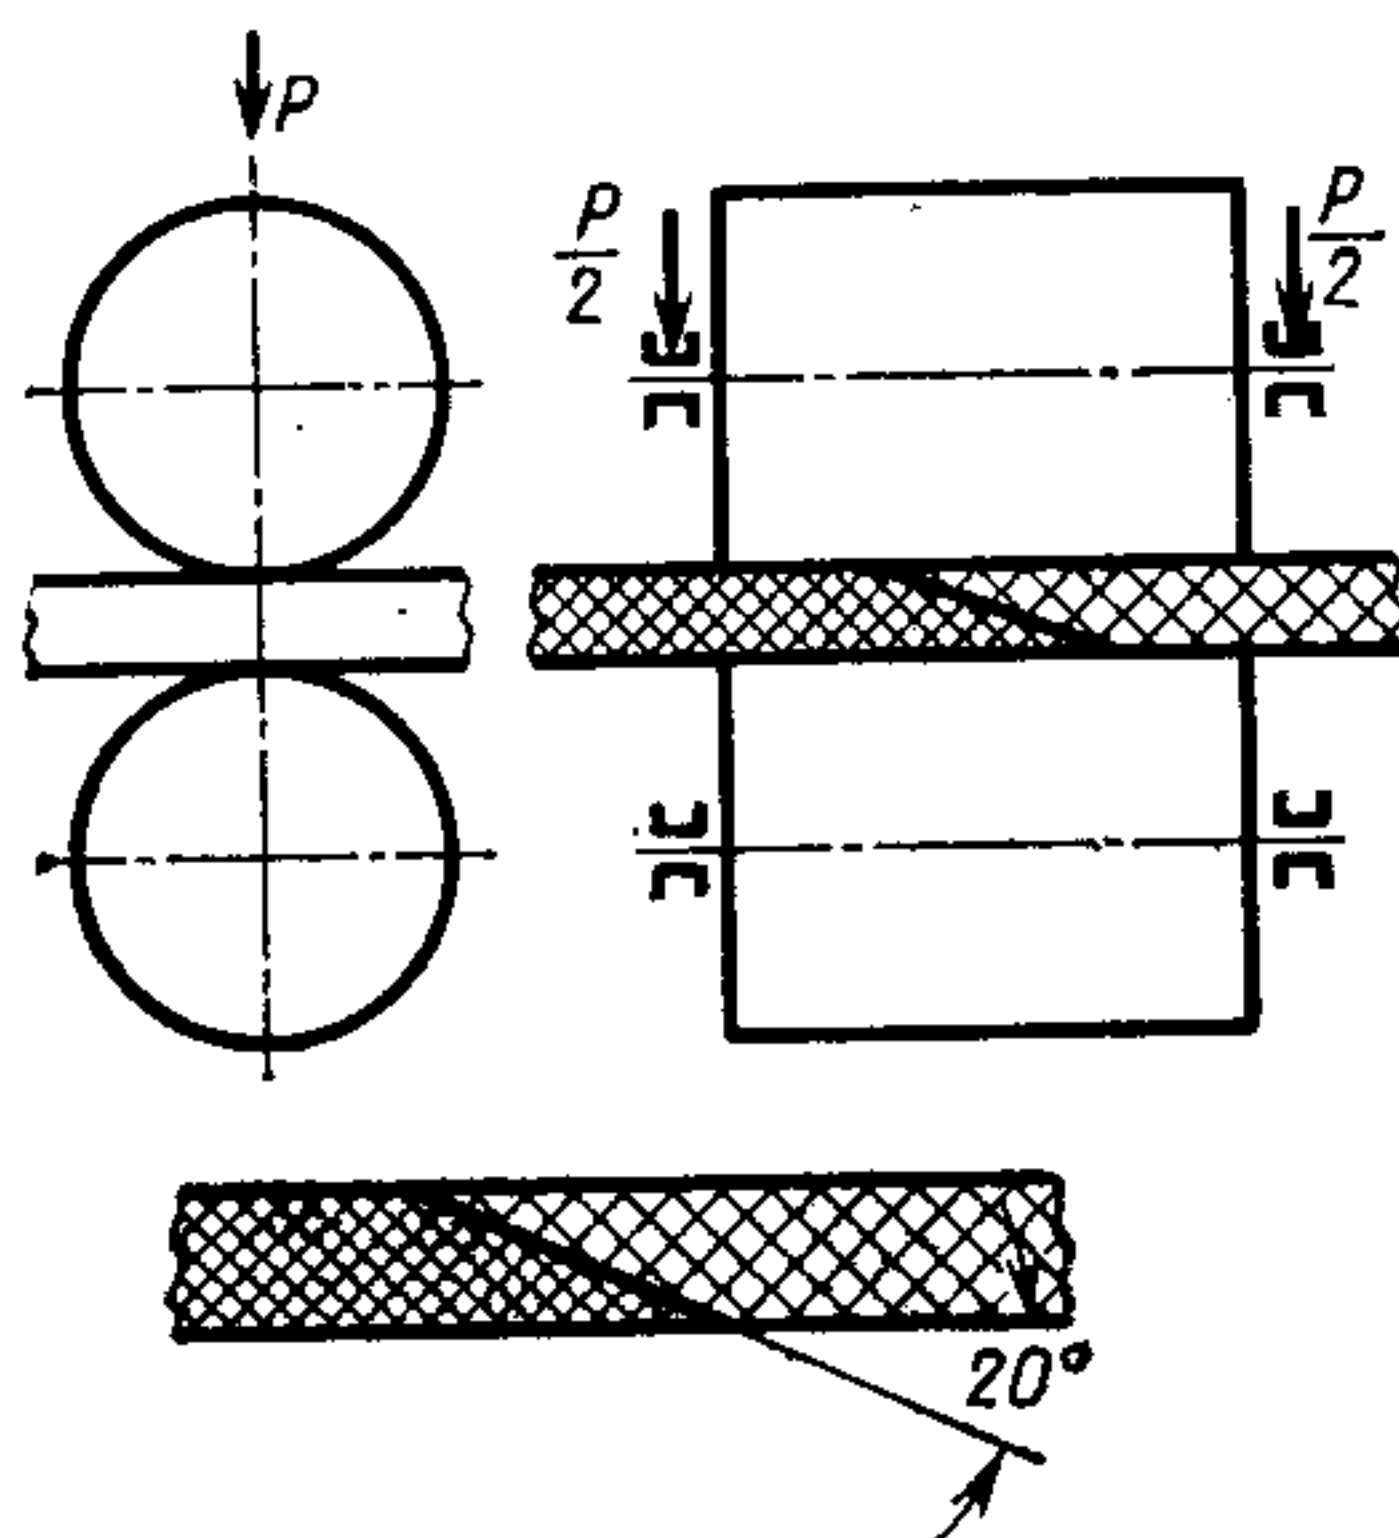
Беспрутковая сварка листов и пленок
